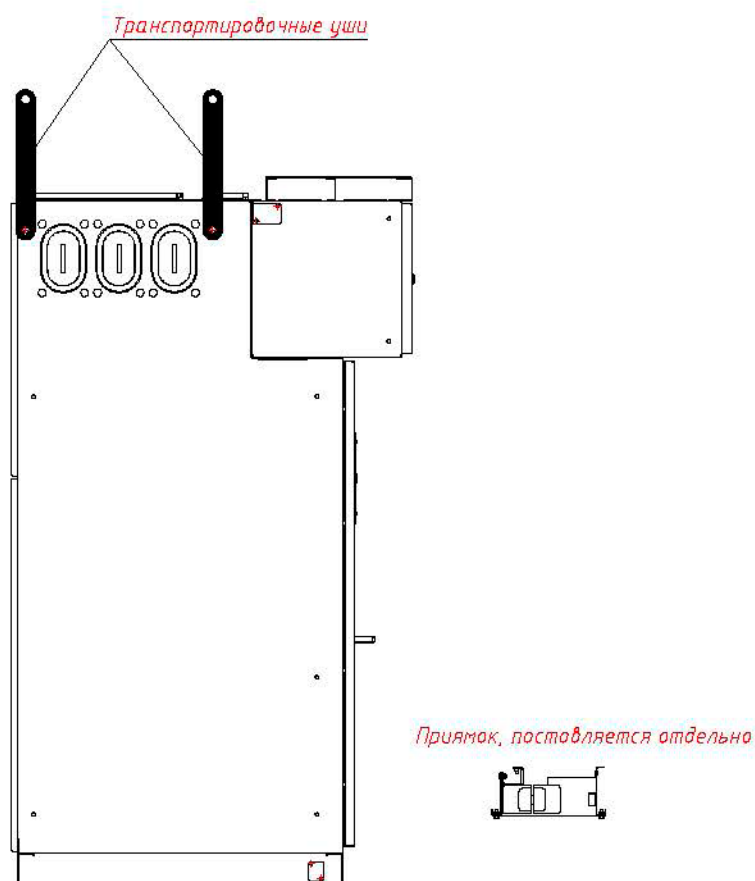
Камера КСО в транспортировочном положении (без упаковки)
